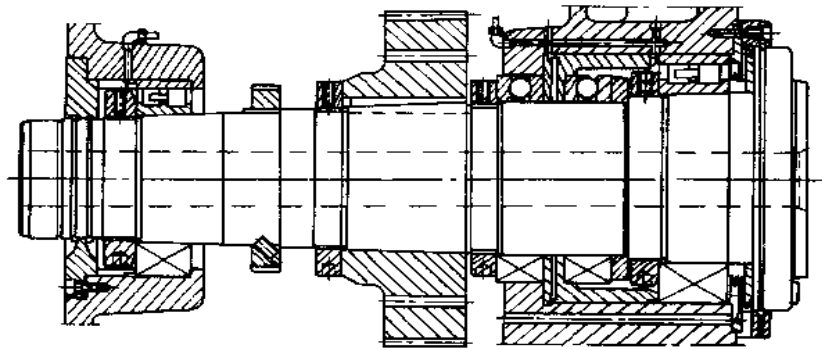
立式轧辊传动装置正齿轮联动机构支承
